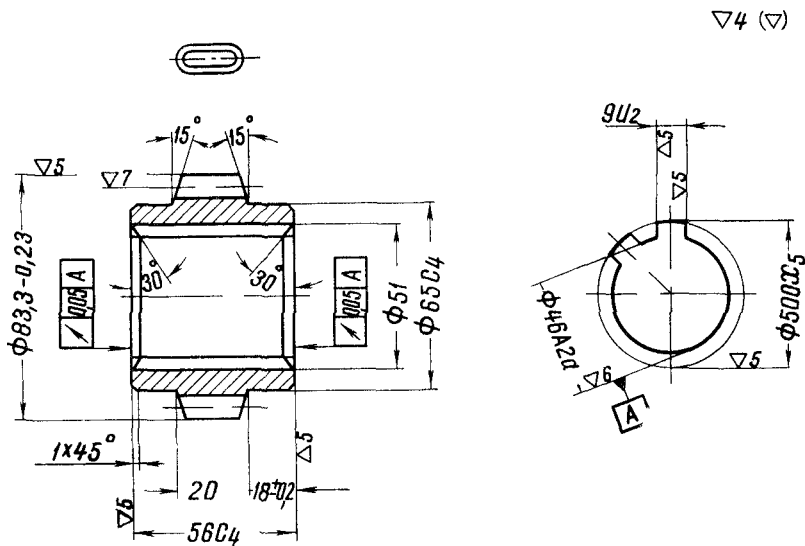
Зубчатое колесо Деталь 6М82 3-48Н
